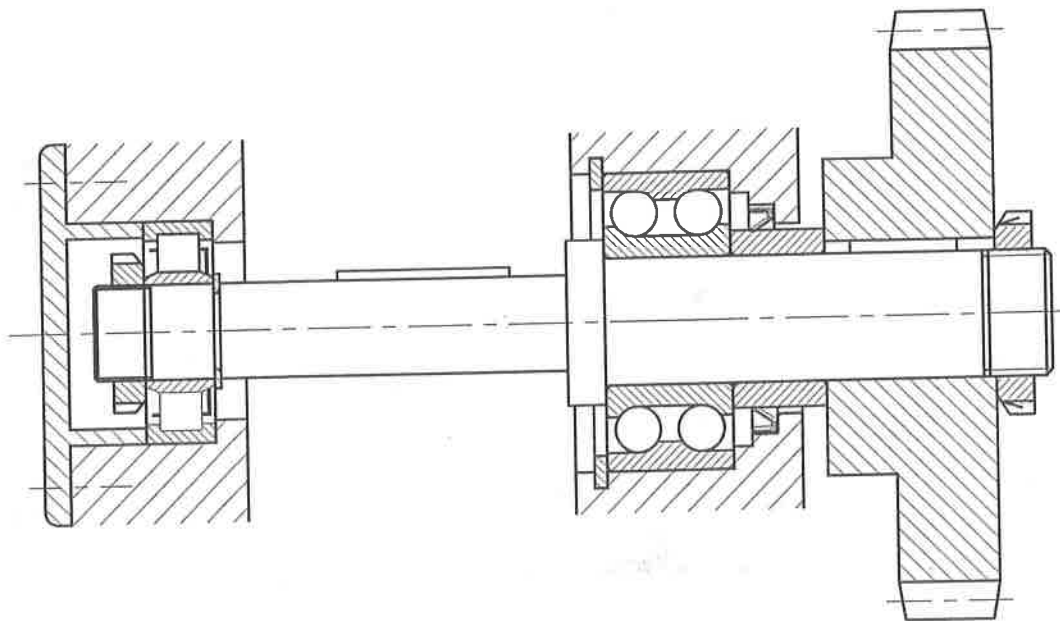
Disposición de rodamientos. Rodamiento de rodillos cilíndricos sin pestaña en aro interior, libre a la izquierda y rodamiento fijo a la derecha.
